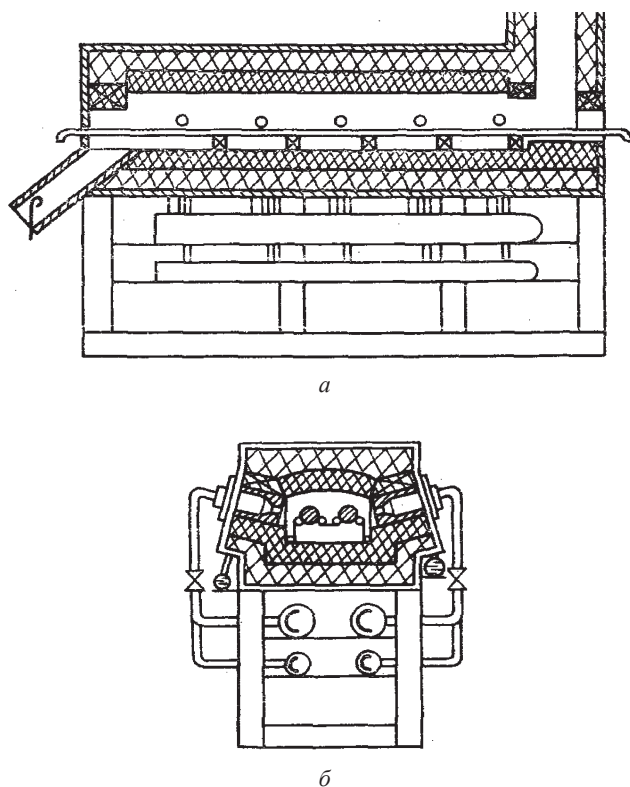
Схема печи скоростного струйного нагрева стальных заготовок производительностью 1000 кг/ч: а – продольный разрез; б – поперечный разрез
